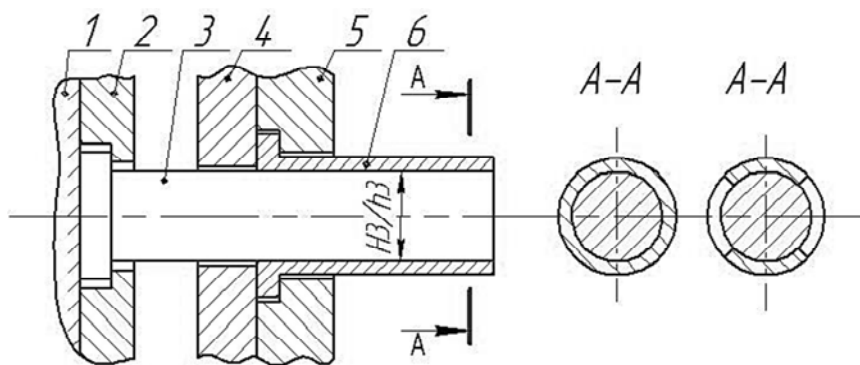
Пример крепления трубчатого сегментного выталкивателя:
